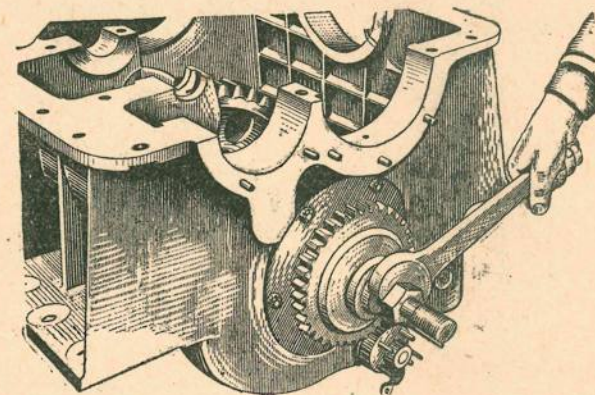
Запрессовка шестерни муфты полужесткого соединения коробки перемены передач при помощи приспособления
